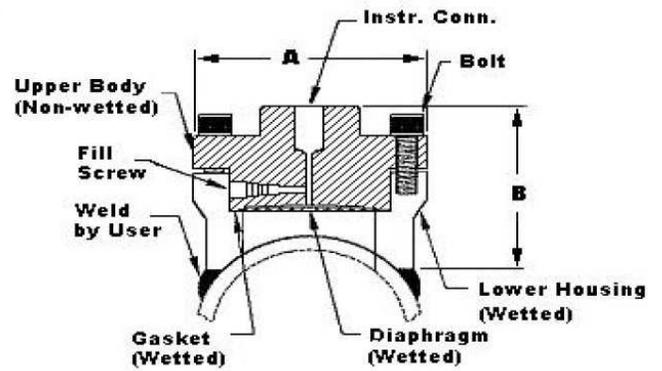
Dimensiuni Capsula Diafragma (3" Saddle Seal)
